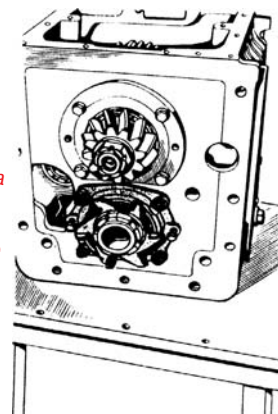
Выпрессовка первичного вала, замена вала, стакана подшипника, подшипника № 210.
